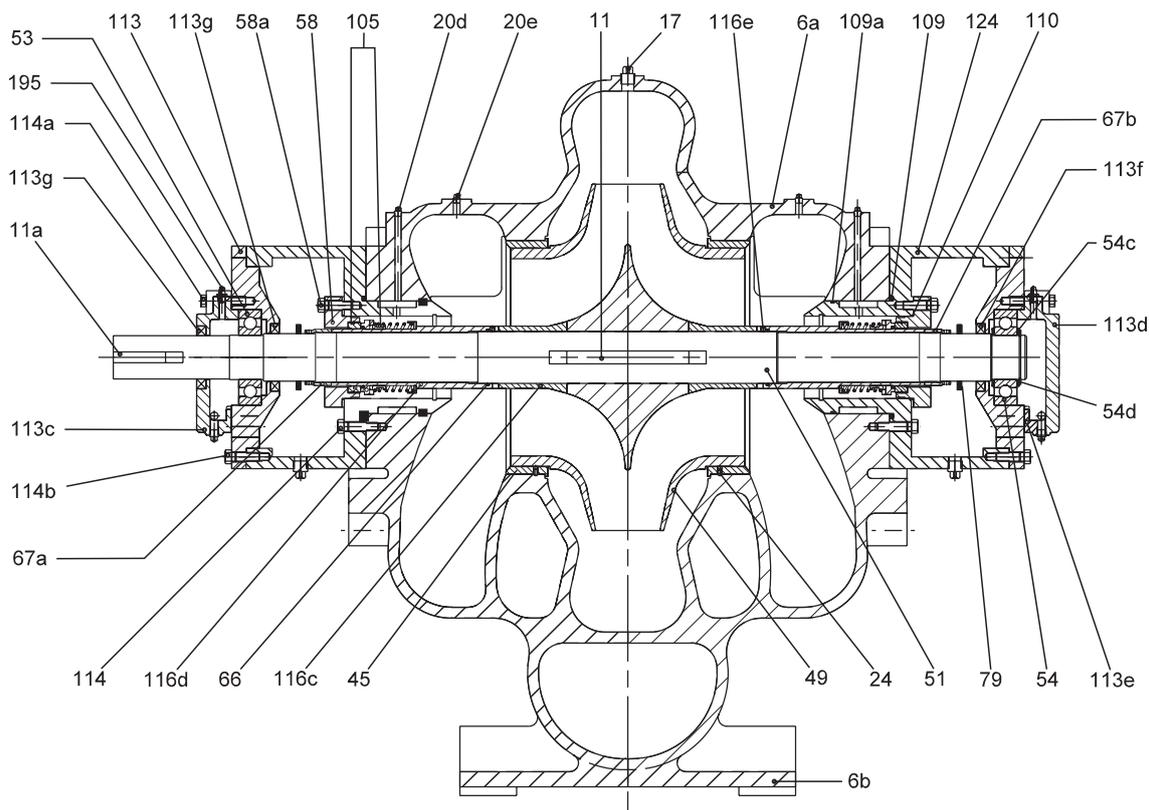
Вид в разрезе, тип конструкции 2 с торцевыми уплотнениями вала
